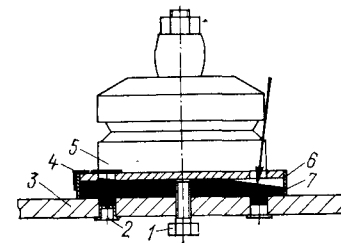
Прокладка из быстротвердеющей пластмассы.
